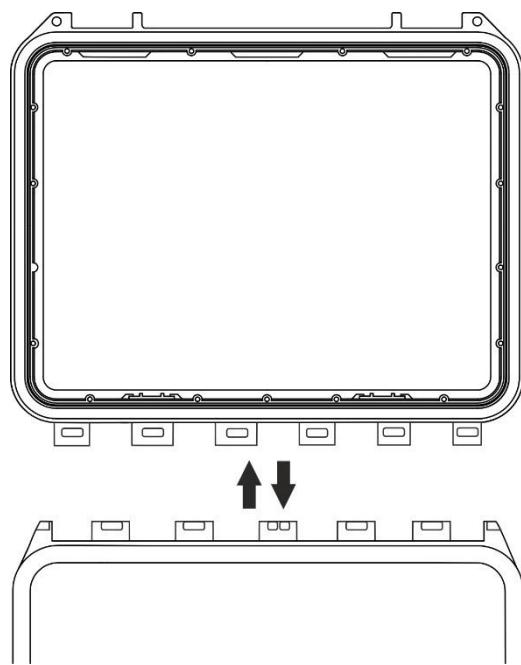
Remoção da tampa da caixa de instrumento - Passo 3
